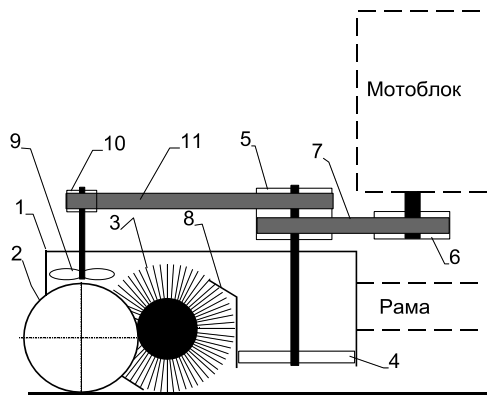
Схематическое изображение навесного оборудования мотоблока для уборки мусора: 1 – корпус; 2 – опорные колеса; 3 – щетка; 4 – устройство измельчения; 5, 6, 10 – шкивы; 7, 11 – ременная передача; 8 – отражатель; 9 – вентилятор
